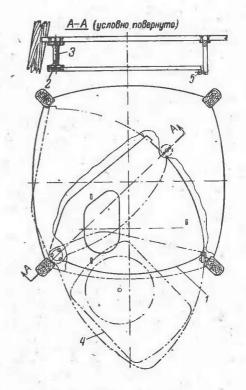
Общий вид проигрывателя, 1— плата; 2— ось; 3— втулка; 4— проигрыватель; 5— поддерживающий ролик.
